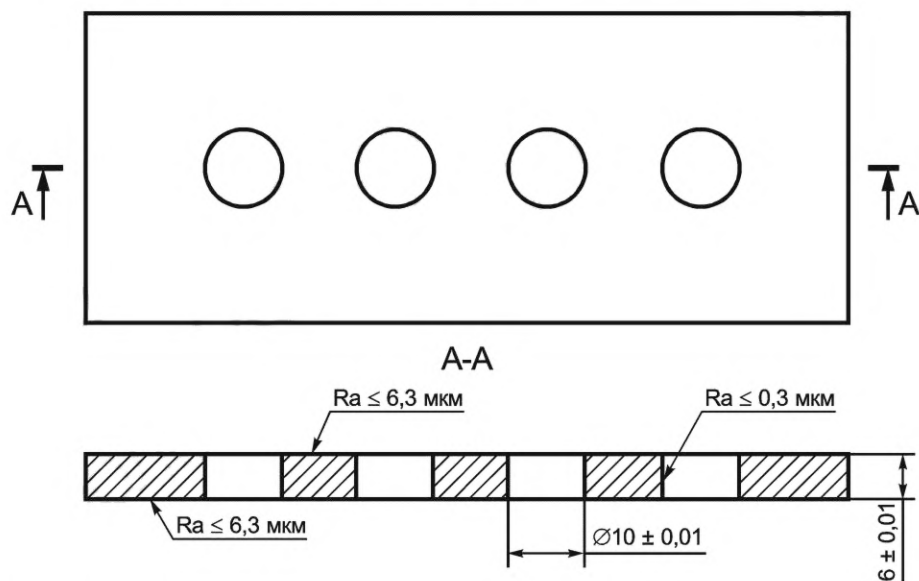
Схема формы для изготовления образцов для испытаний на текучесть
